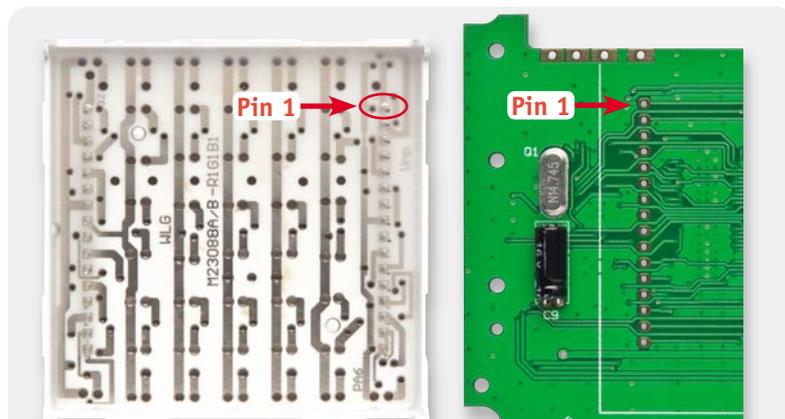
Für die richtige Montage des LED-Moduls ist die hier markierte Position von Pin 1 zu beachten.
